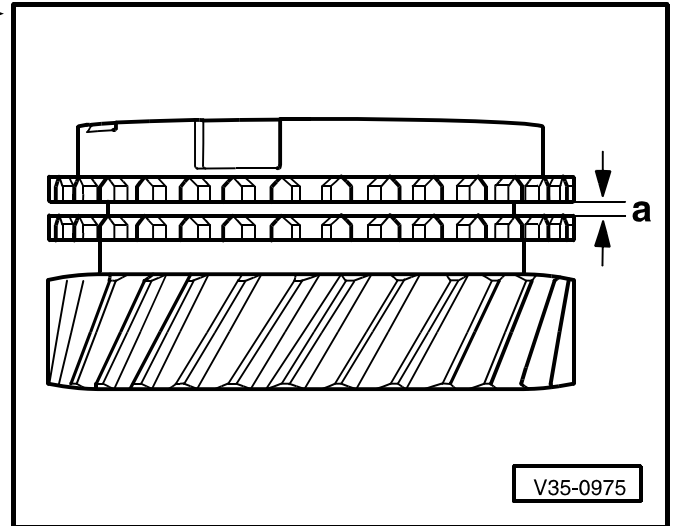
Désassemblage et assemblage du manchon coulissant et du synchroniseur des rapports 3 et 4
